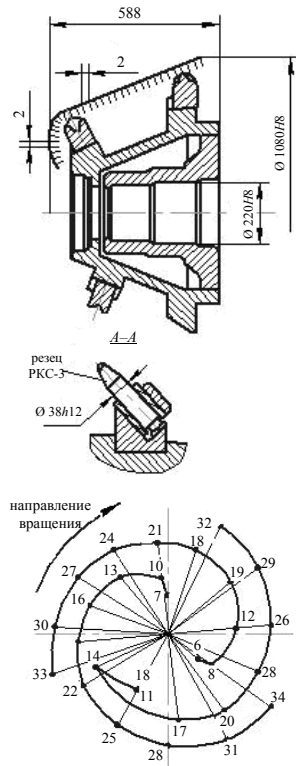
Коронка, оснащенная резцами РКС-3: 1 – 33 – номера резцов
